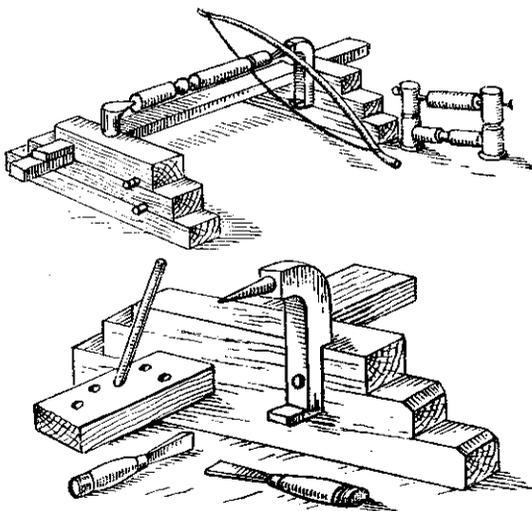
Прimitивный токарный станок с ручным лучковым приводом.
